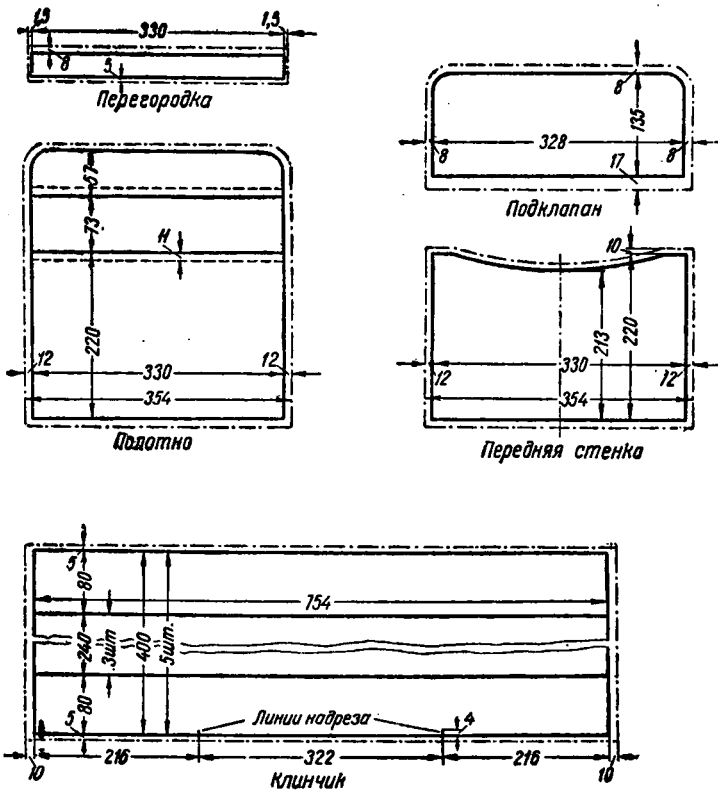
Чертеж деталей портфеля размером 32 × 21 см
